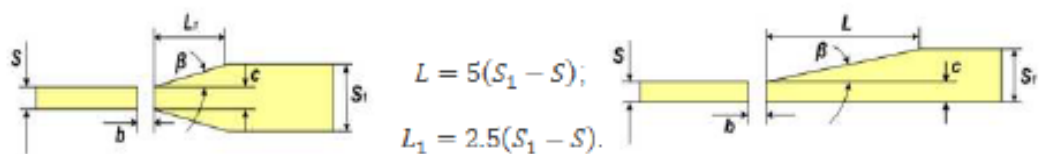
Примеры формы кромок, подготовленных под сварку.
